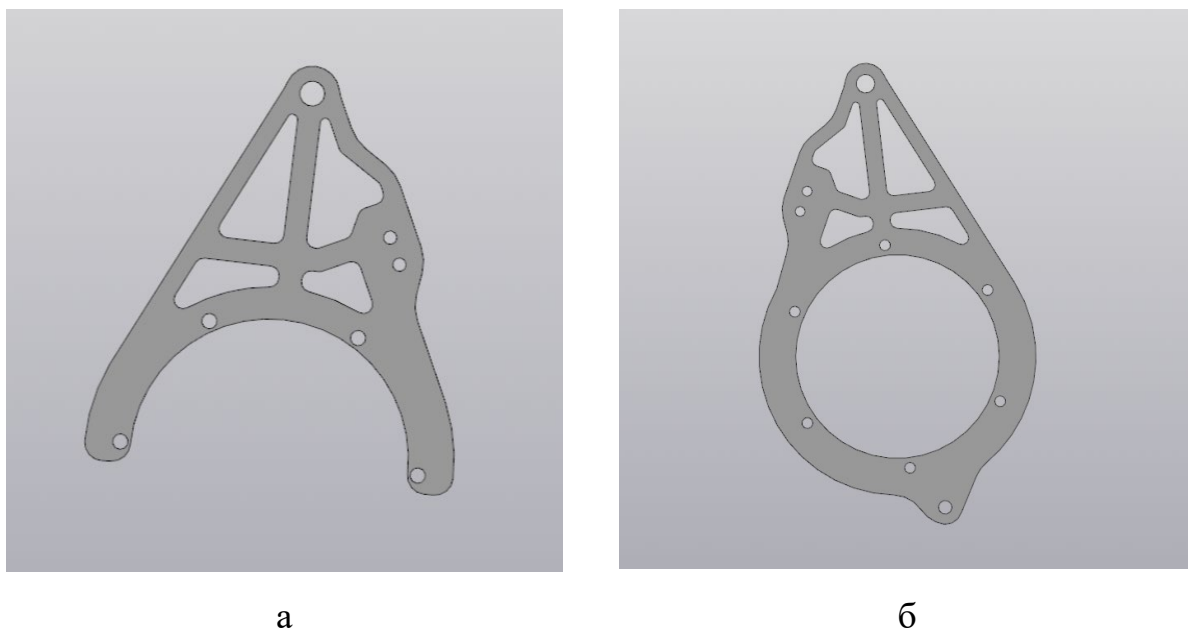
Боковые крепления мотора, выполненные в виде стальных пластин: а – крепление со стороны редуктора; б – крепление со стороны без редуктора
